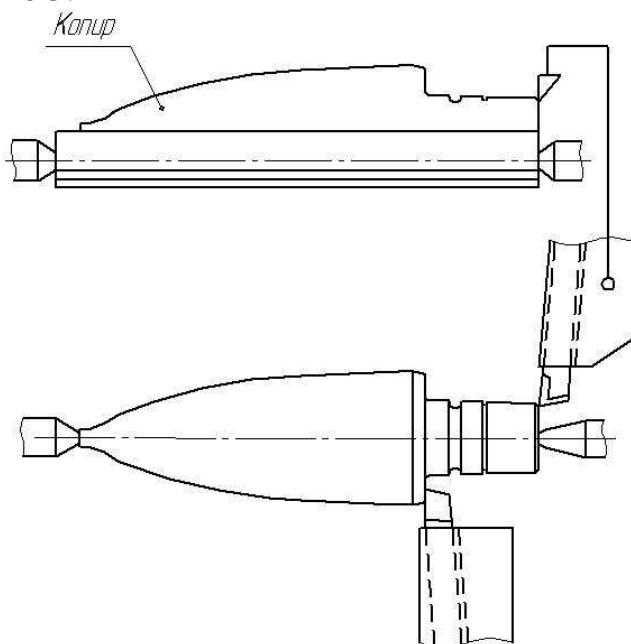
Схема наладки многорезцового копировального полуавтомата для обработки наружной поверхности оправки элонгатора
